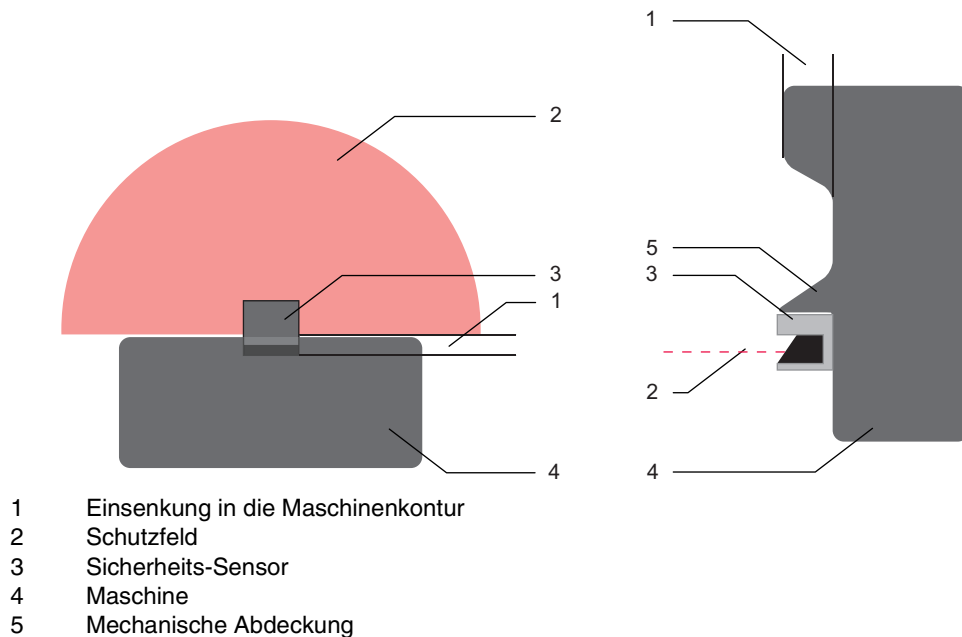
Hintertretschutz durch Einsenken in die Maschinenkontur
